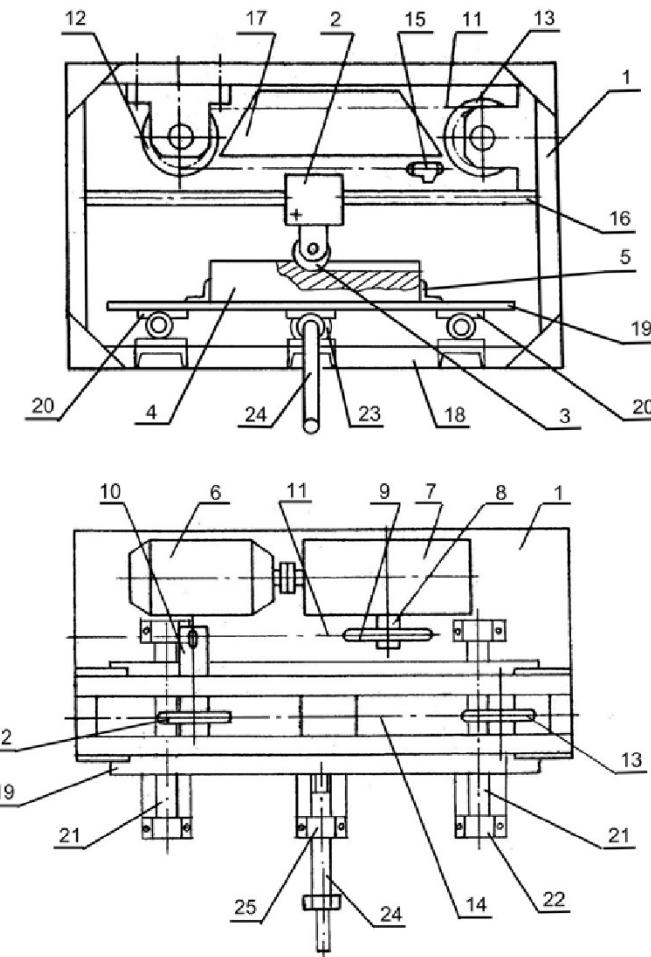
Модернизированный стенд для испытания режущего инструмента рабочих органов строительных и дорожных машин: 1 – опорная рама; 2 – тензометрическая головка; 3 – испытываемый режущий инструмент; 4 – образец грунта; 5 – упоры; 6 – двигатель; 7 – редуктор; 8 – выходной вал; 9 – звездочка; 10 – звездочка ведущего вала; 11 – цепь; 12, 13 – ведущая и ведомая звездочки тяговой цепи; 14 – тяговая цепь; 15 – захват; 16 – направляющие; 17 – шина; 18 – нижняя балка опорной рамы; 19 – несущая плита; 20 – подшипники скольжения; 21 – направляющие механизма поперечной подачи образца; 22 – опоры; 23 – ходовой механизм; 24 – поворотная рукоятка; 25 – опора поворотной рукоятки.
